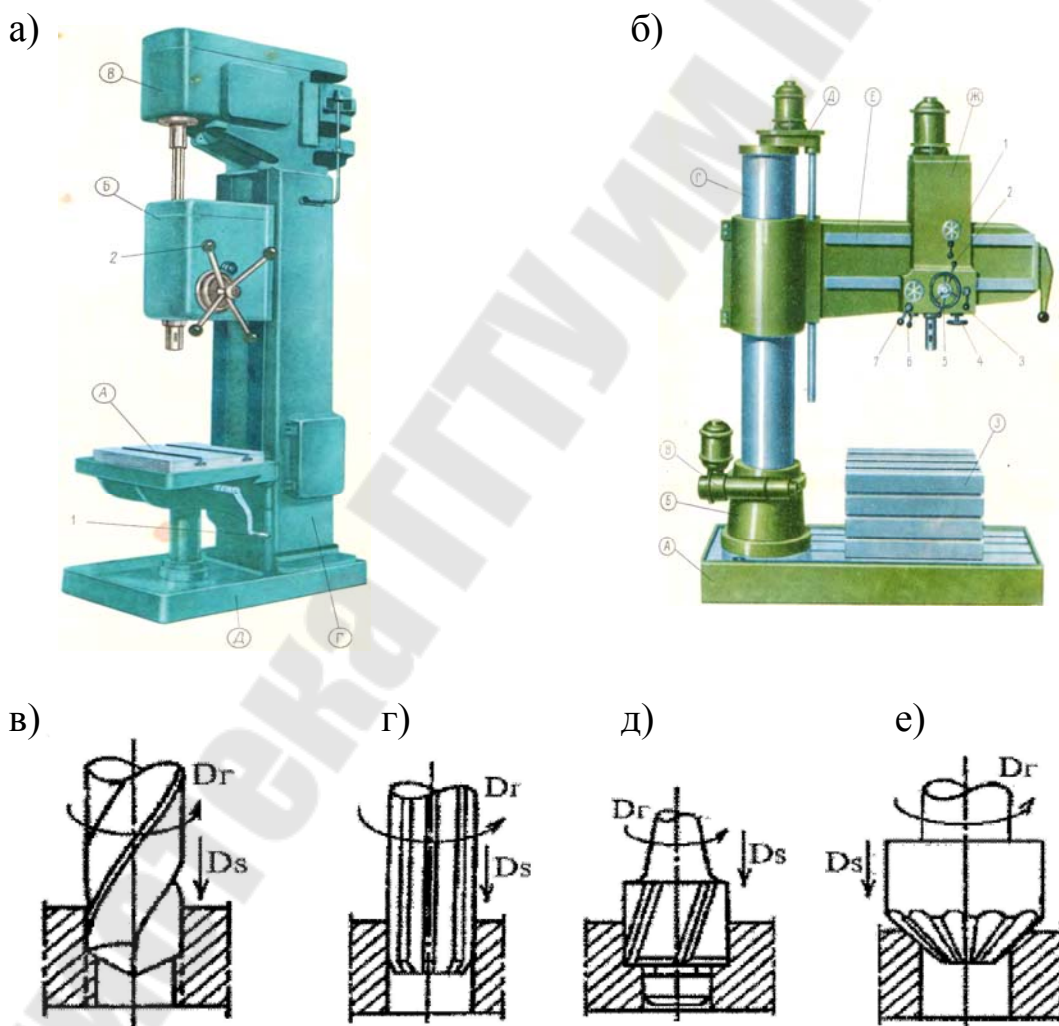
Общий вид вертикально сверлильного (а), радиально сверлильного (б) станков и схемы обработки отверстий (в - е)
